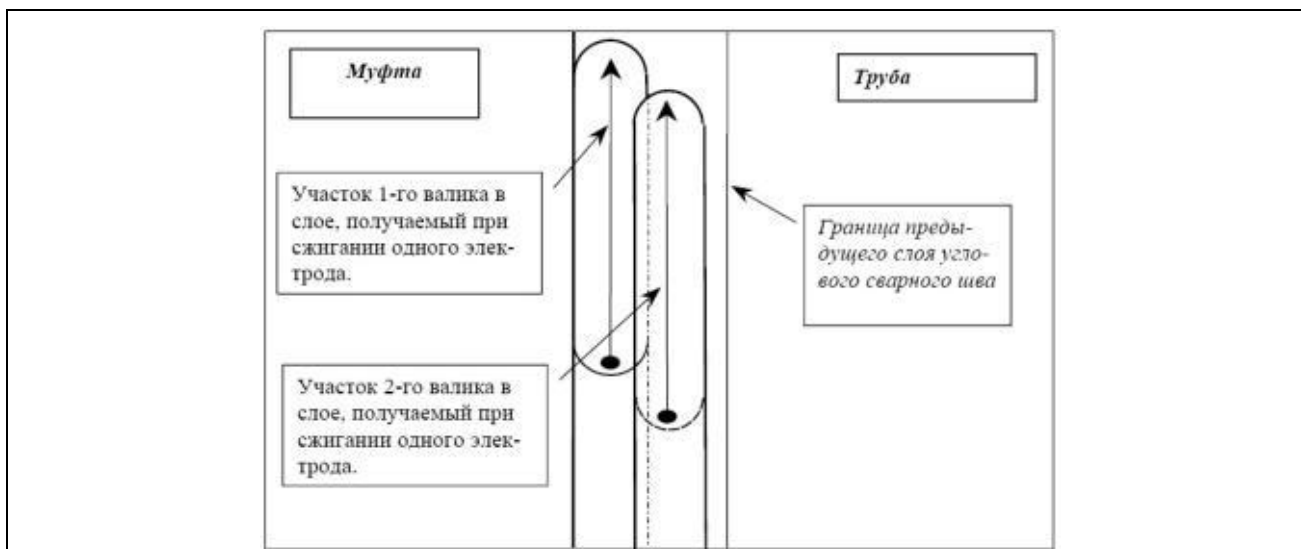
Последовательность сварки наплавочных и заполняющих слоев шва двумя валиками ступенчатым методом
